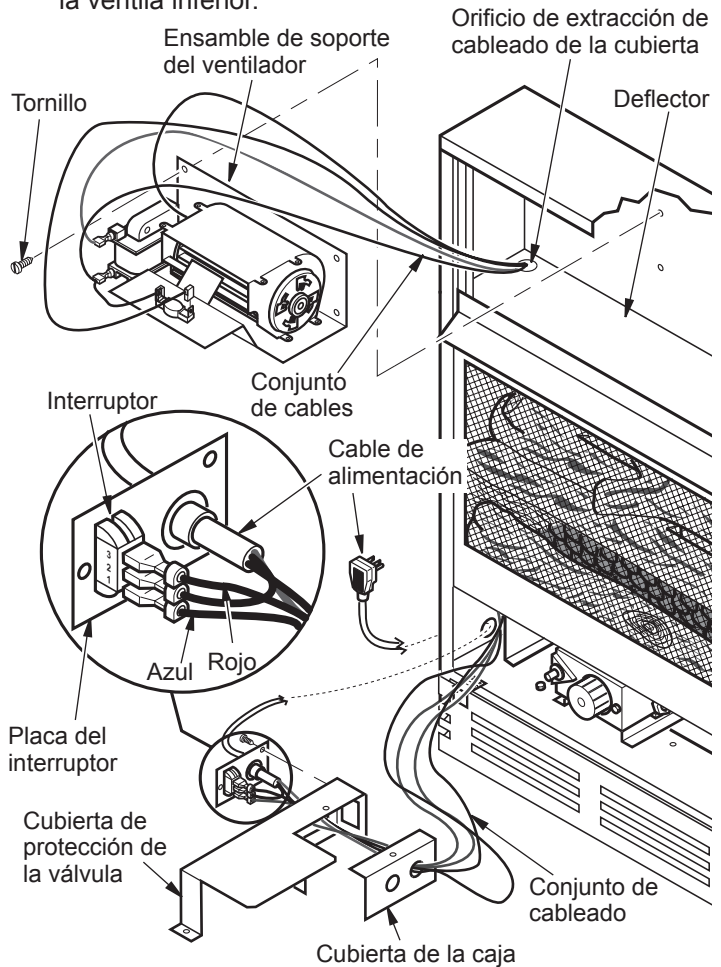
Extracción de la cubierta de protección de la válvula
